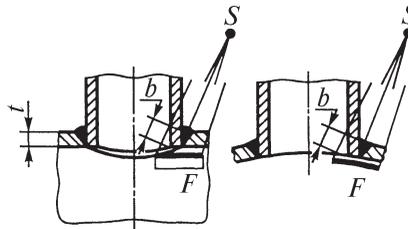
Схема получения снимка для плоского сварного шва и при просвечивании через одну стенку:
